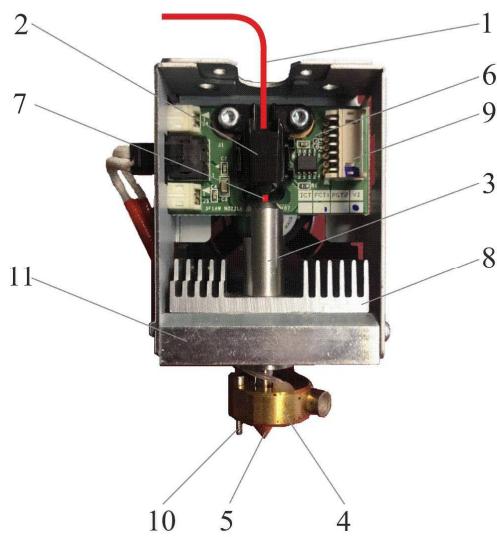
Конструкция печатающей головки 3D-принтера: 1 – пластиковая проволока (расходный материал для печати); 2 – зажим; 3 – направляющая втулка; 4 – экструдер; 5 – сопло; 6 – микроконтроллер печатающей головки; 7 – воздушный термоизоляционный зазор; 8 – радиатор охлаждения; 9 – разъем подключения питания и интерфейса управления; 10 – измерительный щуп; 11 – корпус
